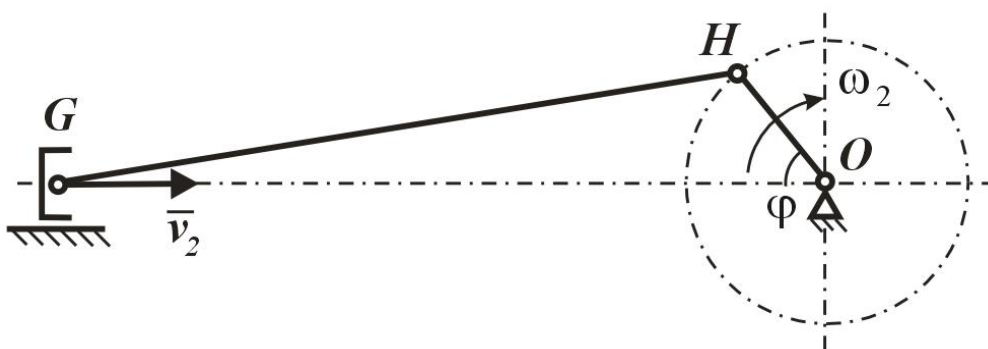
Кинематическая схема возвратно-поступательного движения наплавочной горелки
